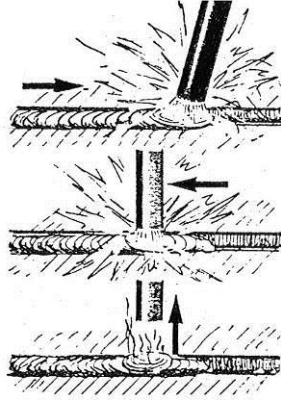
Bazı tip elektrodun kaynak metali geçişi büyük damlalar hâlinde olması
